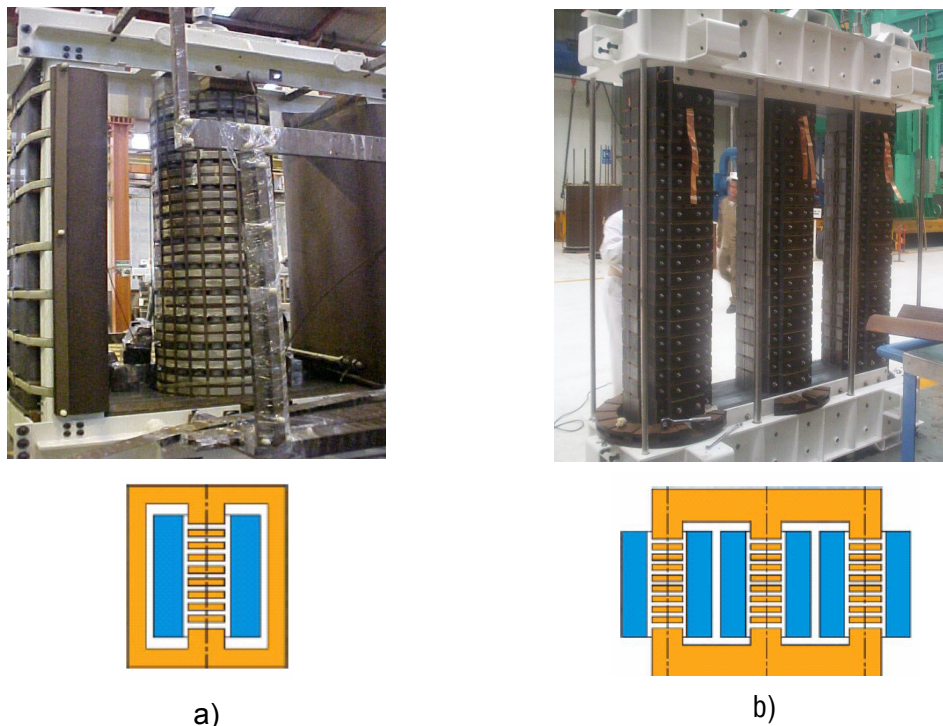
Reactores sumergidos en aceite: (a) tipo acorazado, (b) tipo columna (cortesía de IEM).
